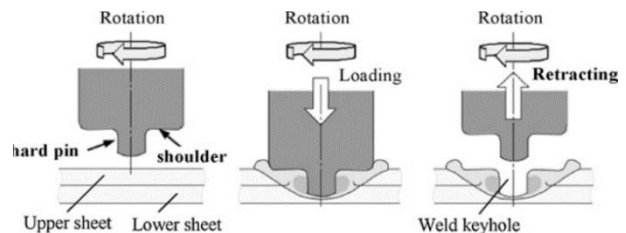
Proceso Completo de Soldadura por Fricción-Agitación [7].
